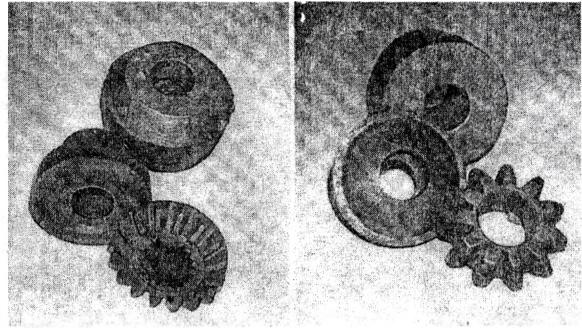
Литая заготовка, поковка и готовая шестерня дифференциала МАЗ-5336 из чугуна
